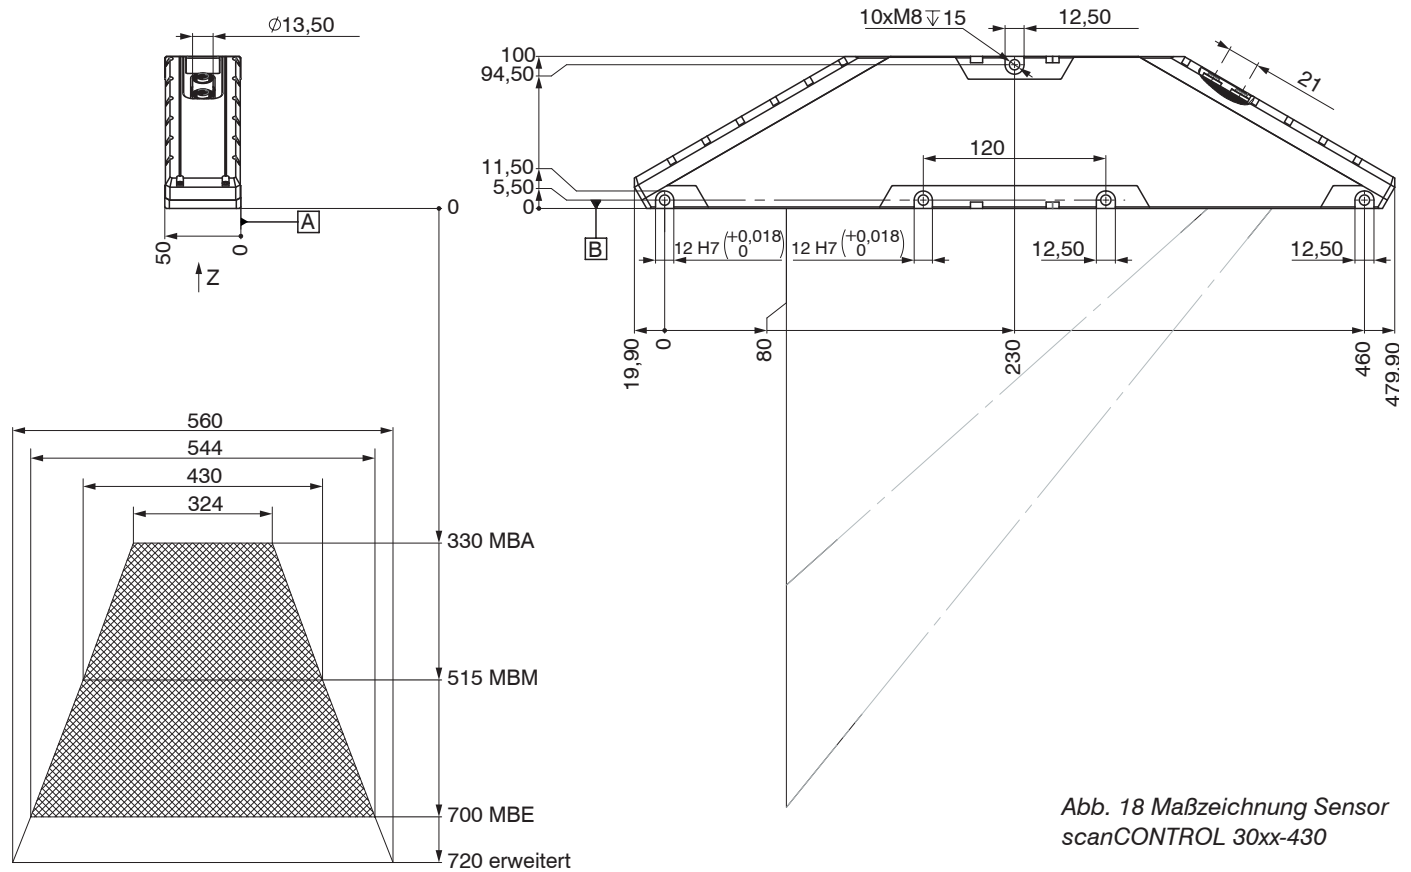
Maßzeichnung Sensor scanCONTROL 30xx-430
